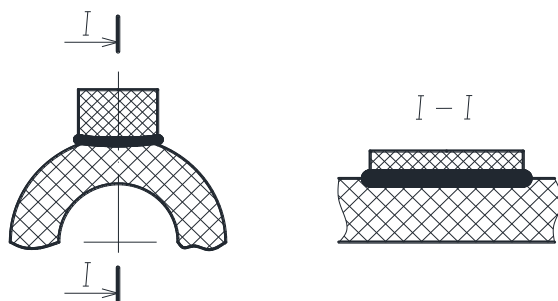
Конструктивные элементы шва сварного соединения (швы Н4)
